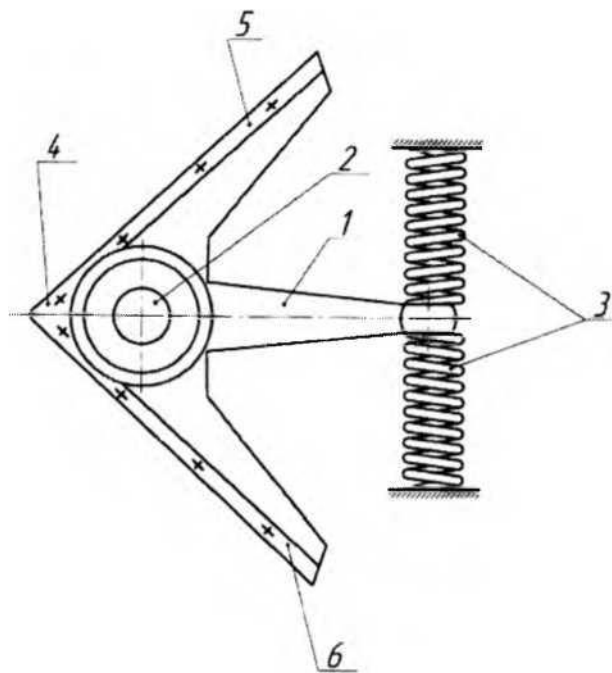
Робочий орган культиватора [15], вид зверху
